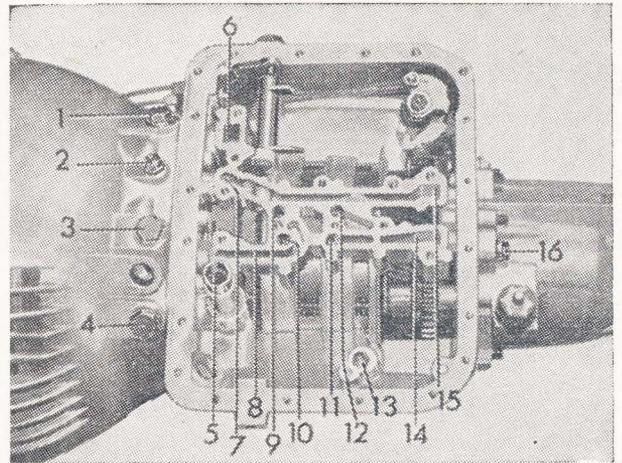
Transmission vue de dessous (carter d'huile enlevé)
